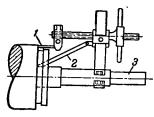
Приспособление для вытаскивания роторных стержней.
